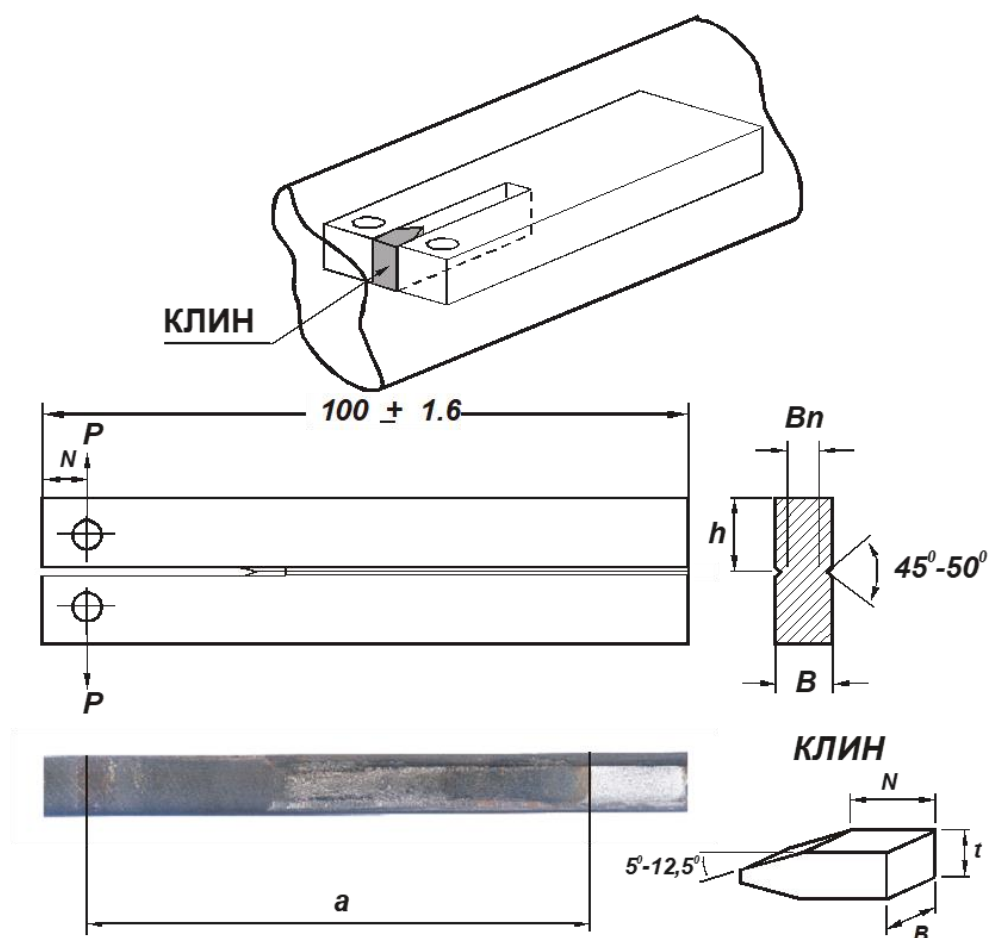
Схема вырезки и вид ДКБ-образца
